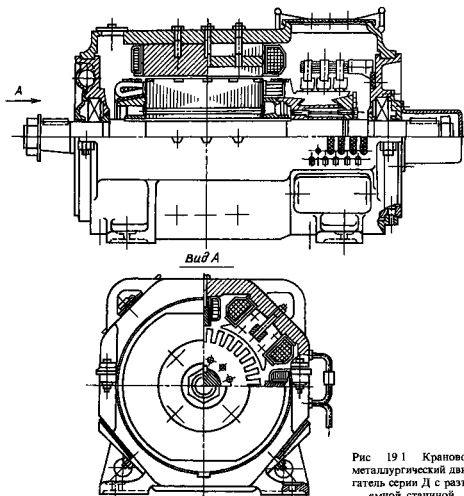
Краново-металлургический двигатель серии Д с разъемной станиной
